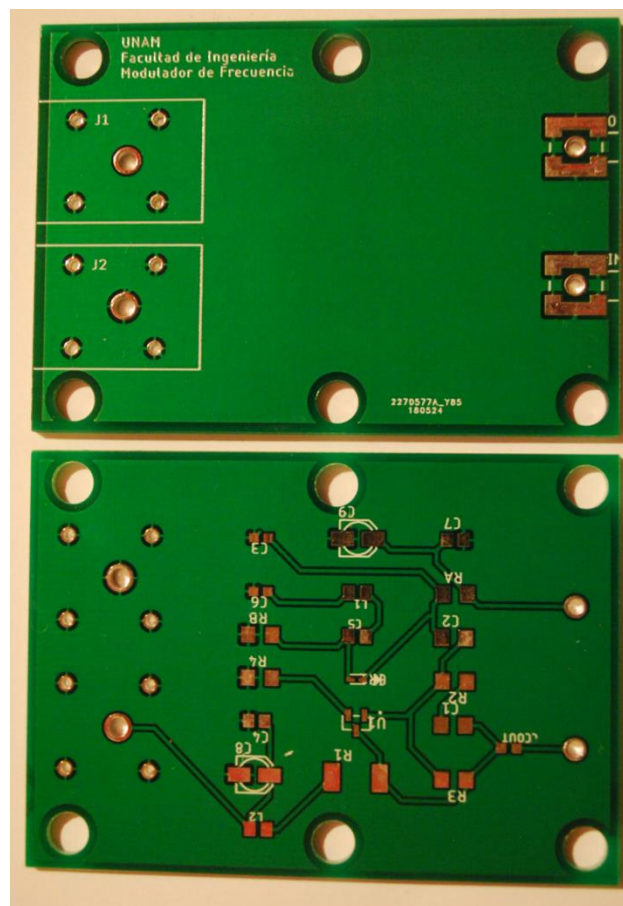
Tarjeta PCB del modulador de frecuencia.
